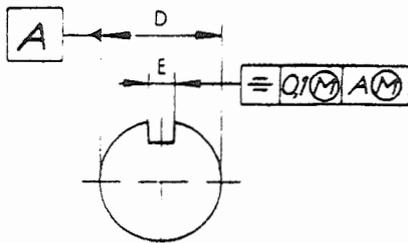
Aplicação da Tolerância de Simetria a um plano médio.
